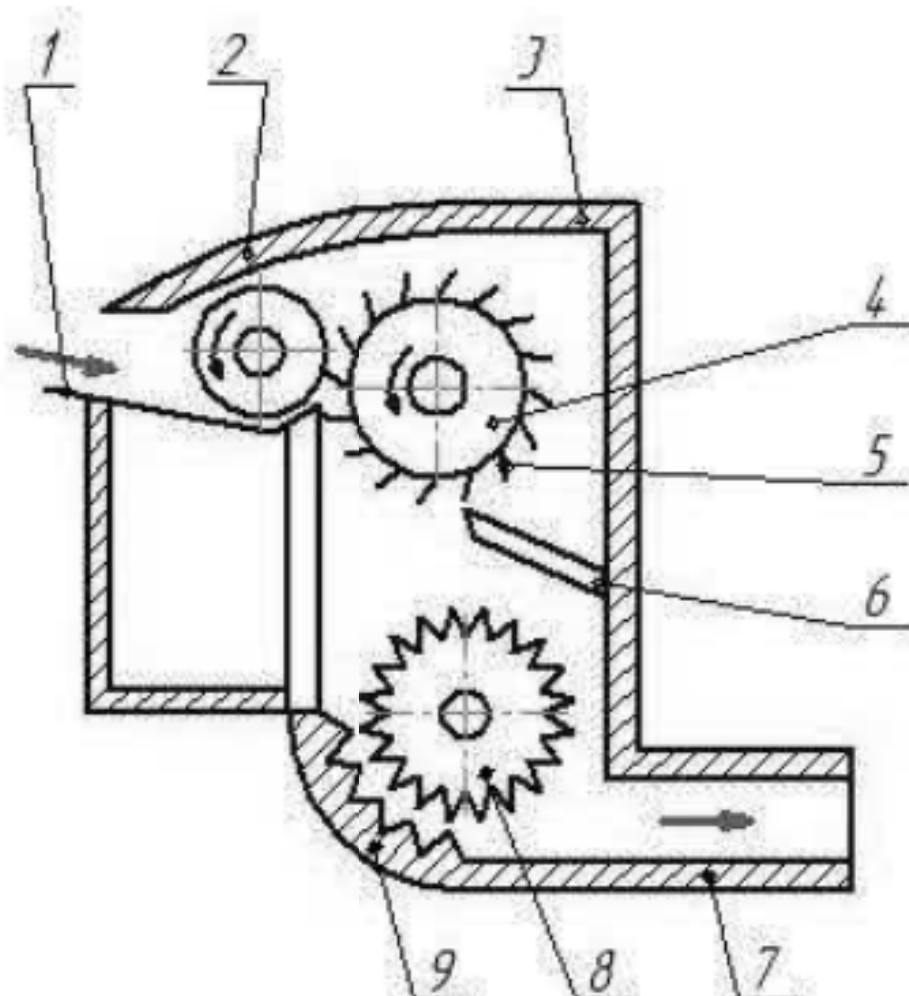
гольчасто-фрезерний шліфувальний верстат
